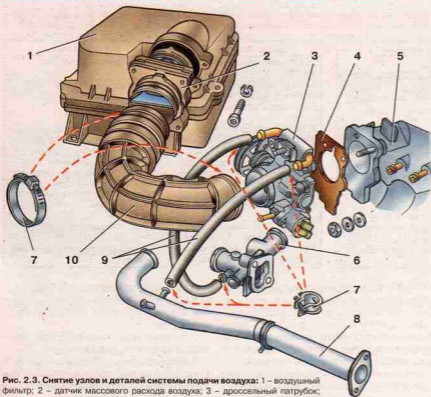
Снятие узлов и деталей системы подачи воздуха: 1 – воздушный фильтр; 2 – датчик массового расхода воздуха; 3 – дроссельный патрубок; 4 – уплотнительная прокладка; 5 – ресивер; 6 – выходящий патрубок системы охлаждения двигателя; 7 – хомуты крепления шлангов; 8 – подводящая труба насоса охлаждающей жидкости; 9 – шланги подогрева дроссельного патрубка; 10 – шланг впускной трубы
